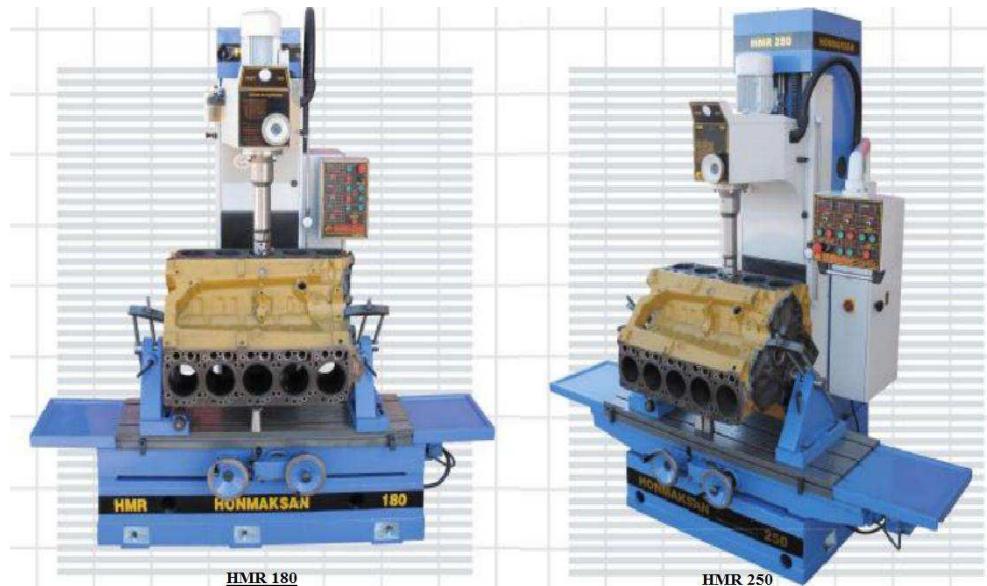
Вертикально-расточные станки для расточки блоков цилиндров и фрезерования плоскости HMR 180 и HMR 250.
